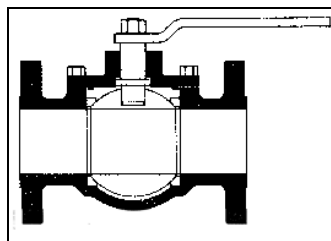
Válvula de Bola. Fuente: CRANE (1992).
